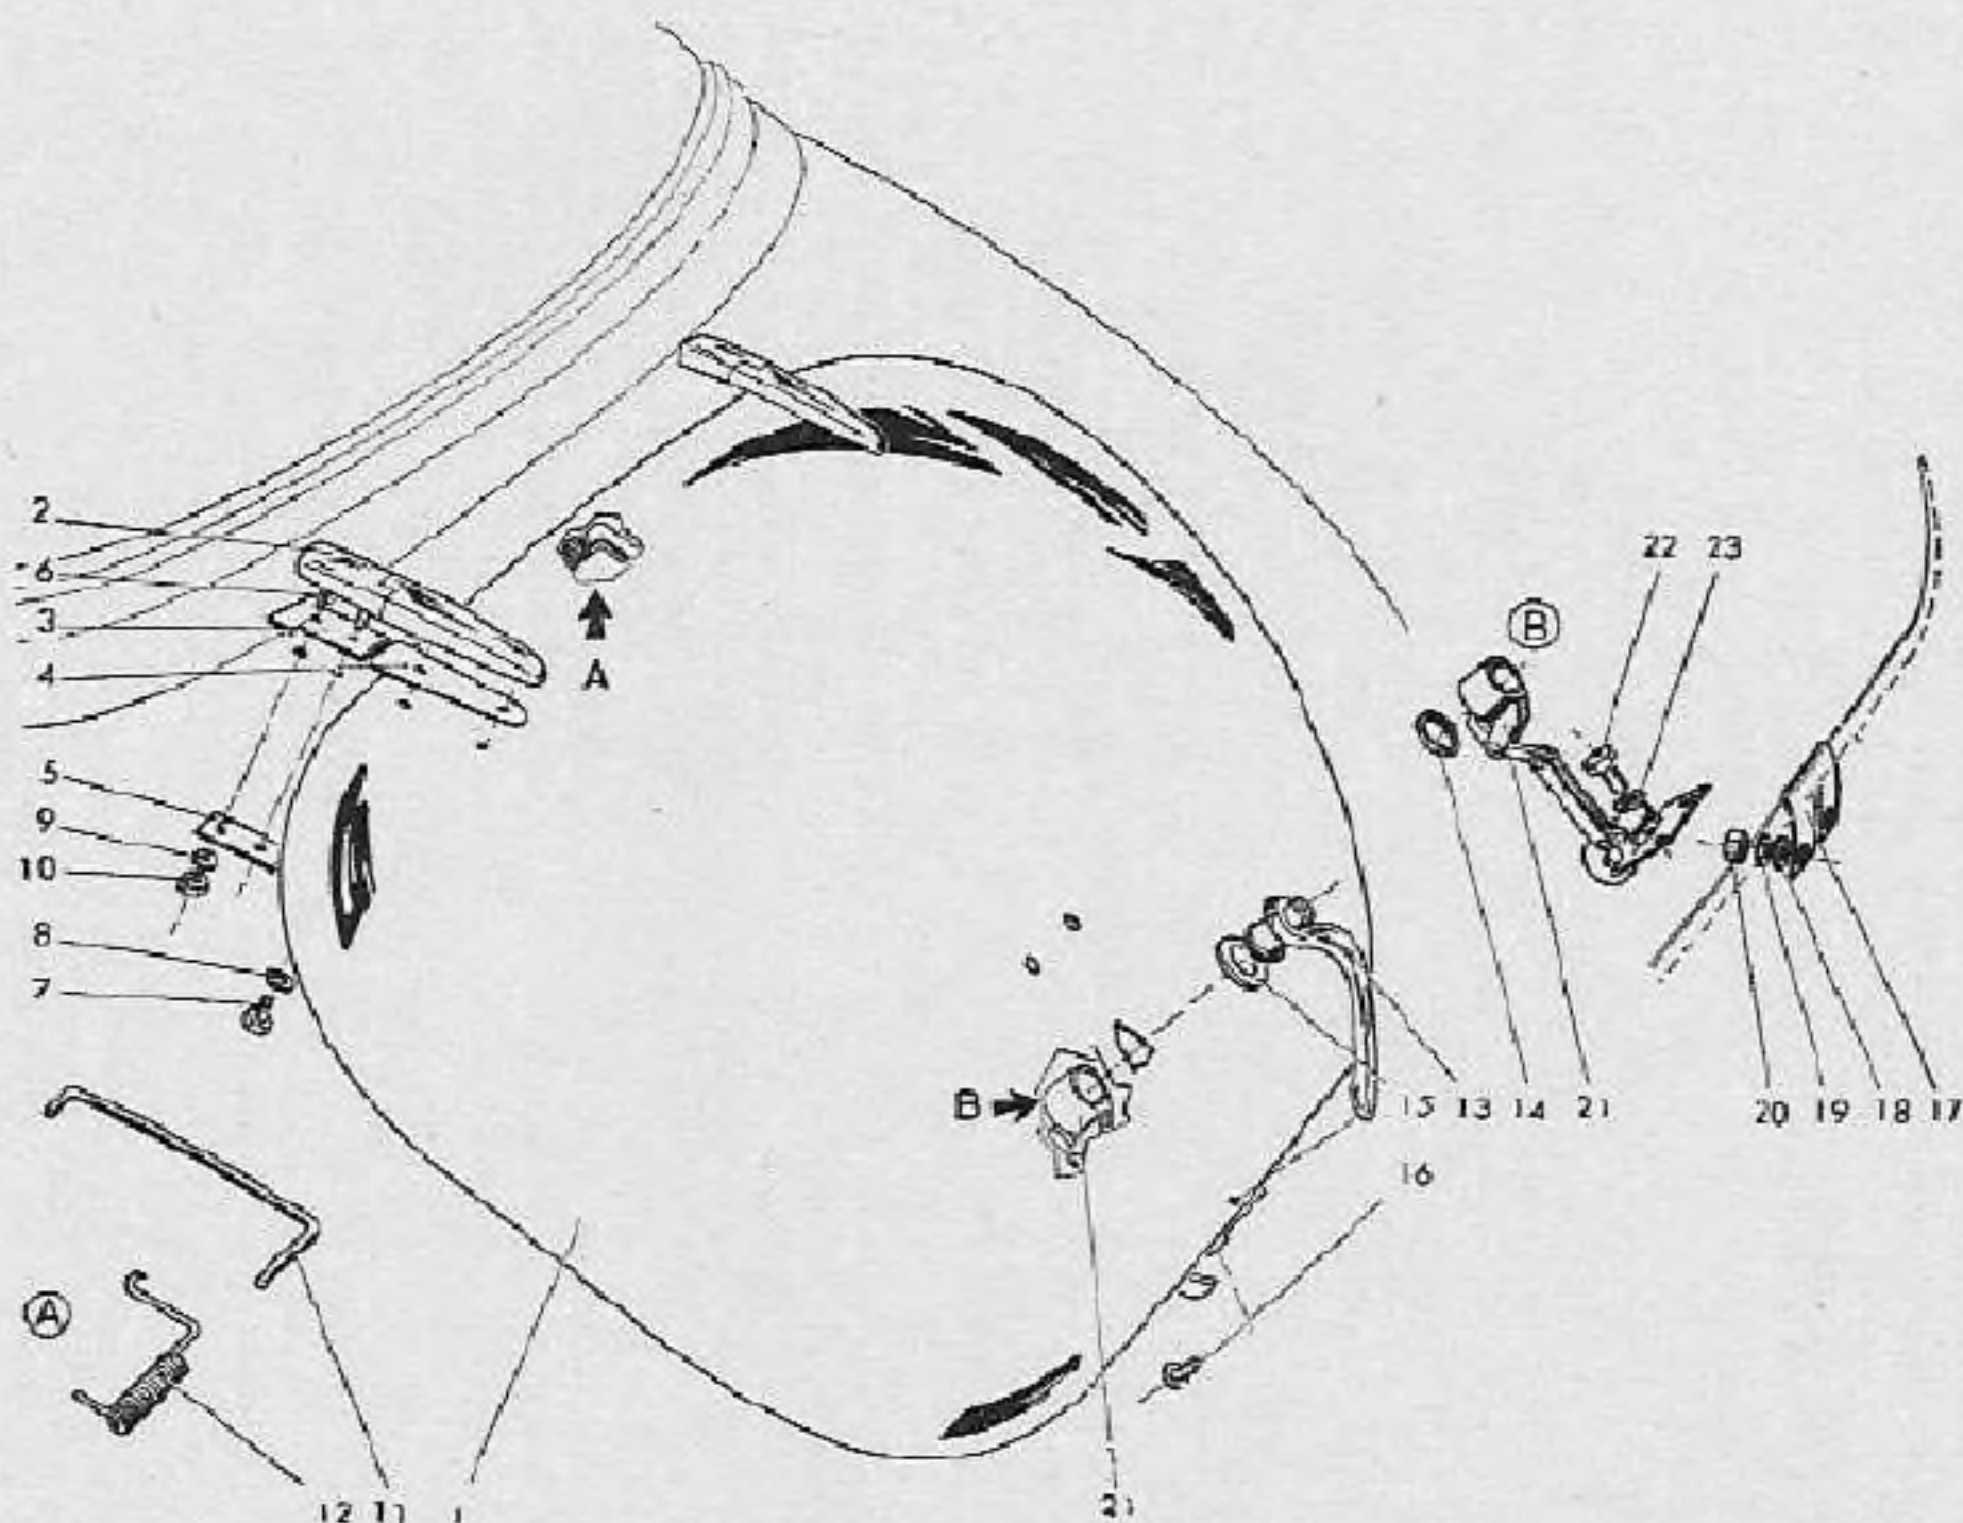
Tapa del baúl portaequipaje del Sedan AU 1000 4p.
